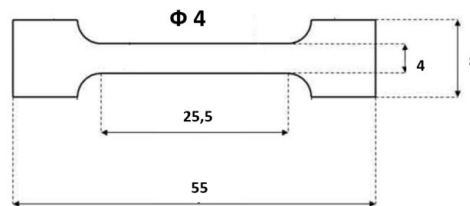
Dimensions d'une éprouvette cylindrique Φ 4.
